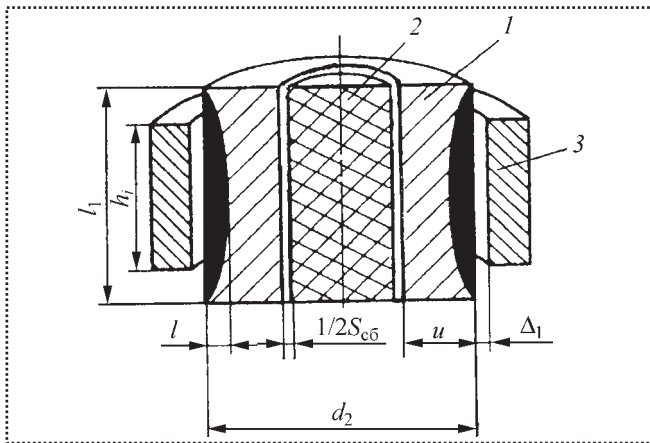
Основные элементы соединения после нагрева: 1 – втулка; 2 – фреза; 3 – нагревательный элемент
